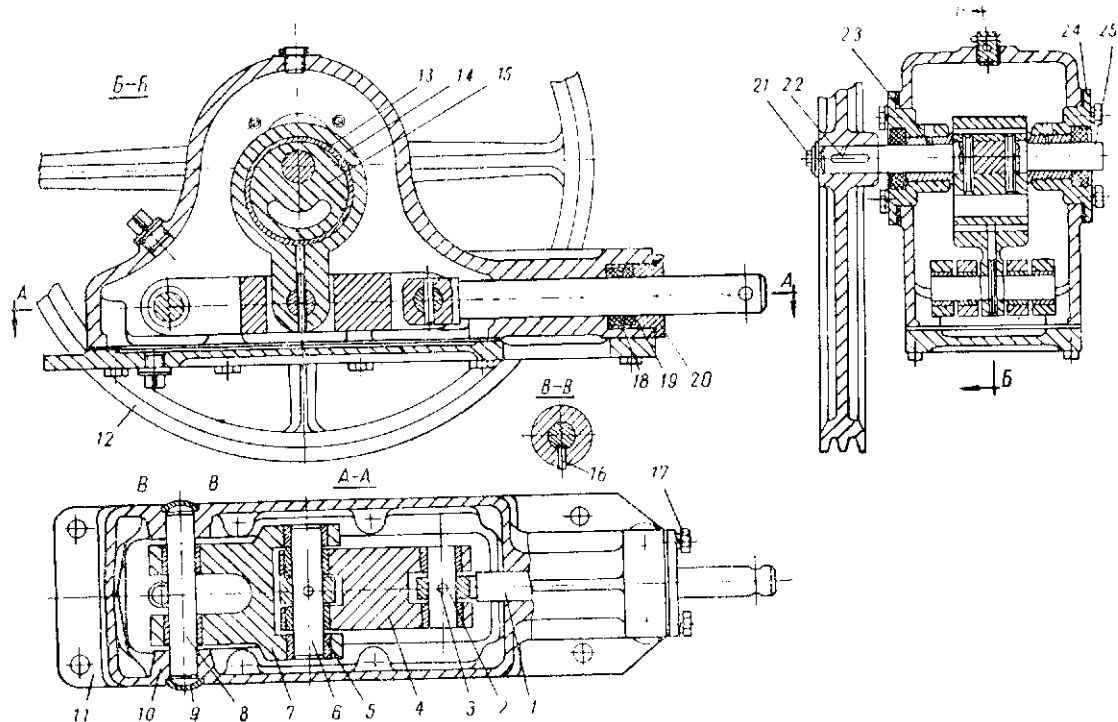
Схема эксцентрикового механизма привода продольных кормушек кормораздатчика:
